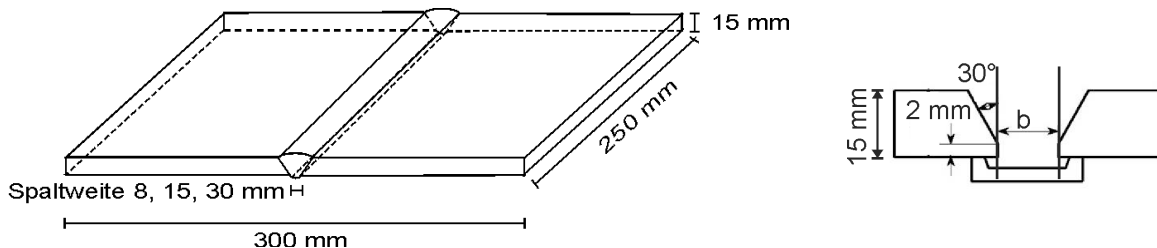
Geometrie der Kleinproben (links: Dimensionen des Stumpfstoßes; rechts: Fugenvorbereitung)
